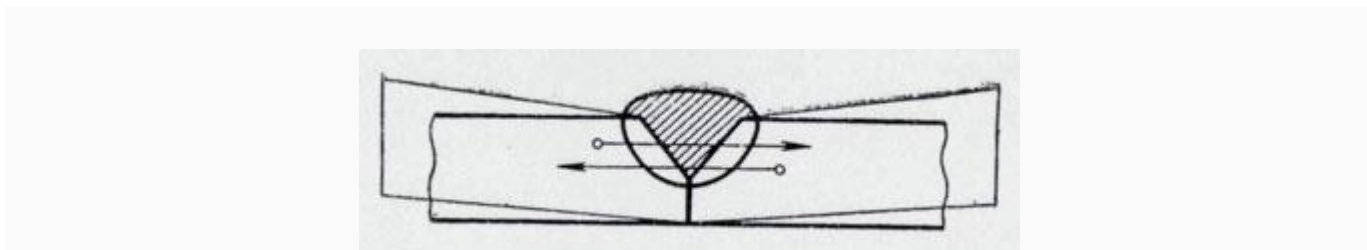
Угловая деформация при сварке стыкового соединения [2]
